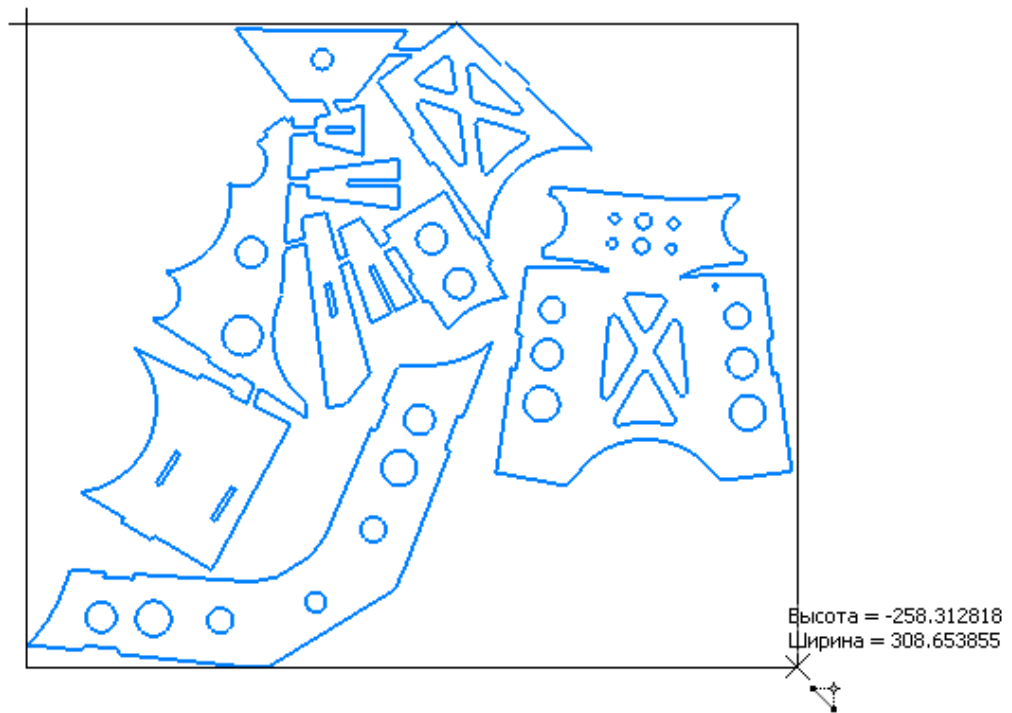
Эскиз деталей для изготовления деталей стального кулака на лазерном станке
